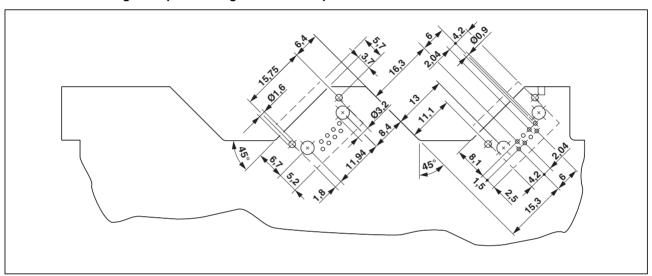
Maßzeichnung der Leiterplatte des Gehäuses bei Verwendung des Anschlusstechnik-Trägers RJ45
